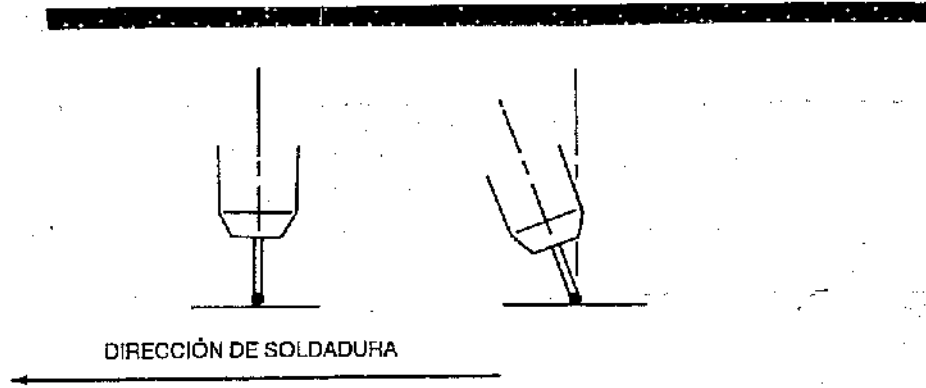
Efecto de la posición del electrodo y de la técnica de soldadura
